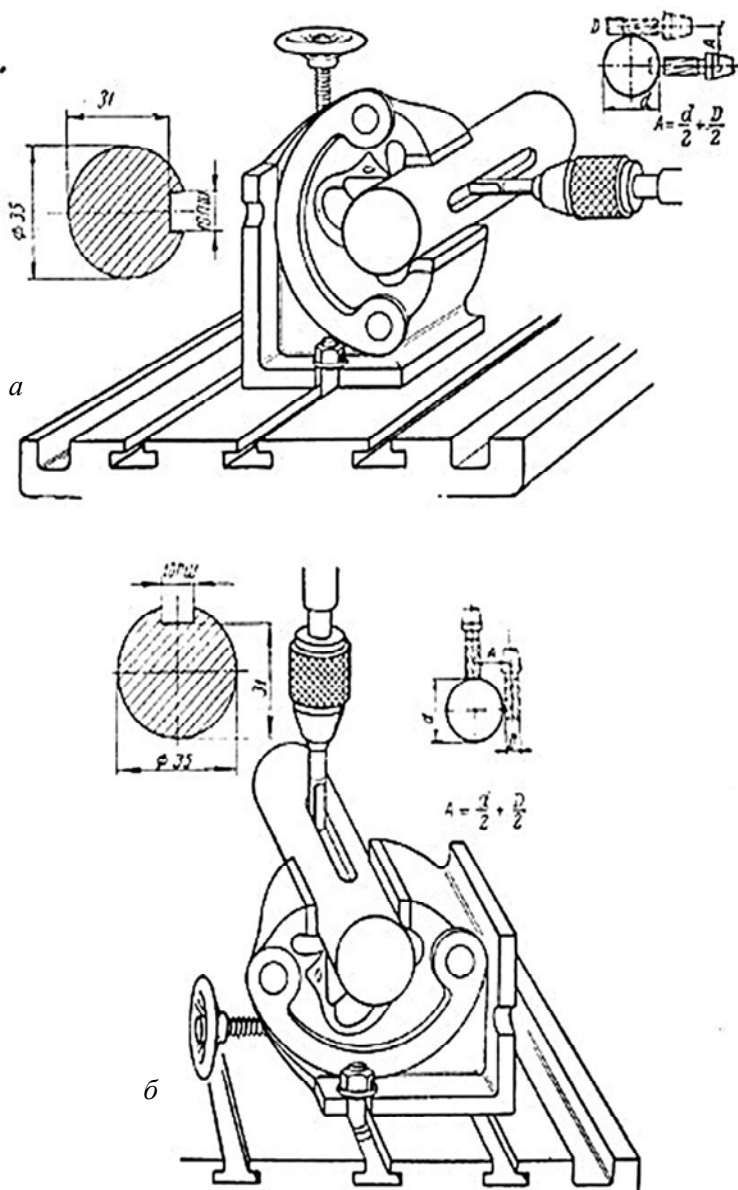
Фрезерование закрытой шпоночной канавки в валу:
